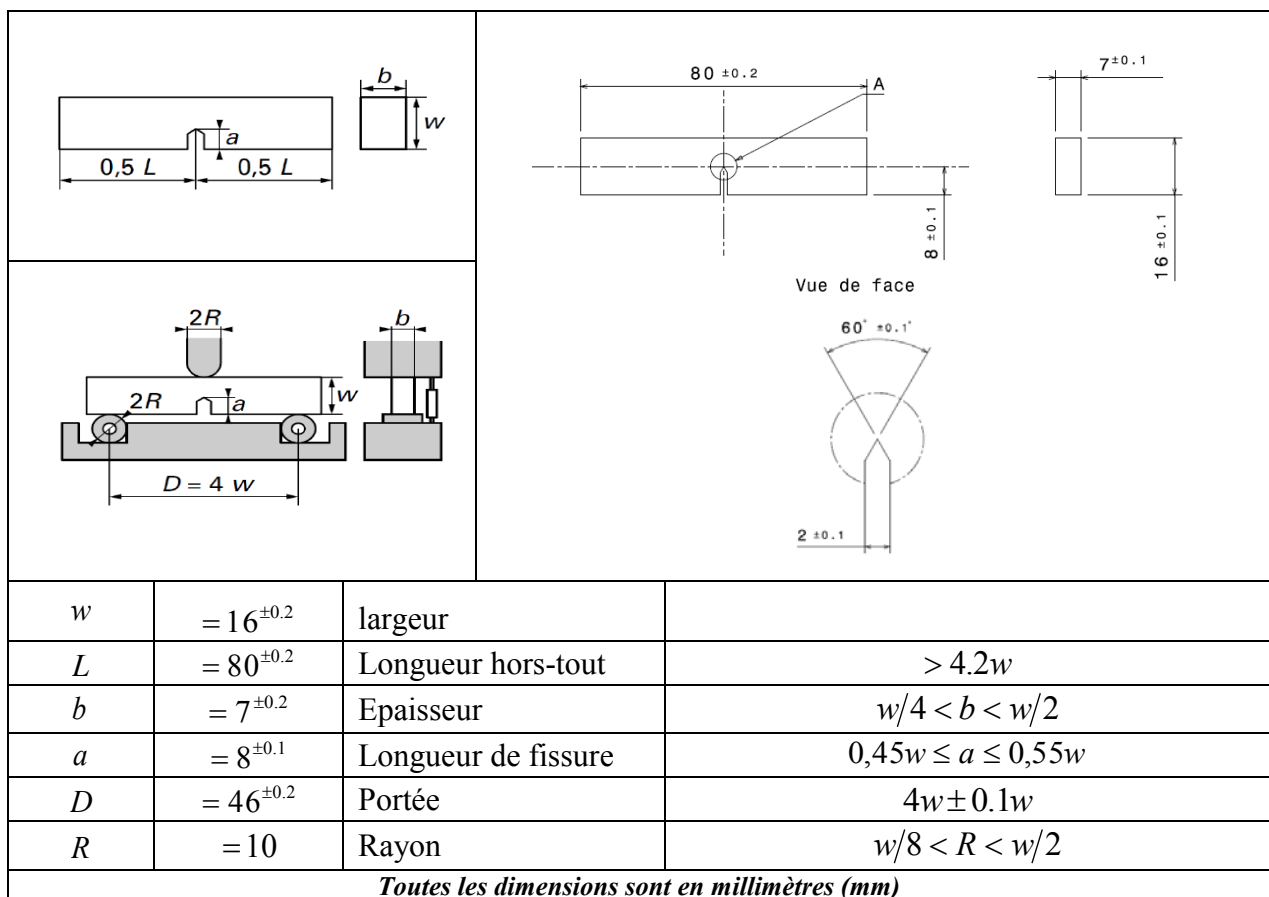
Éprouvette SENB (Single Edge Notched Bend)
